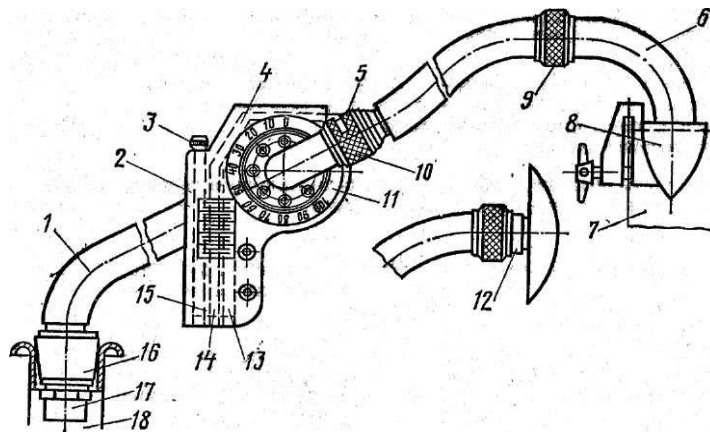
Загальний вигляд і схема підключення газового витратоміра КИ-4887-ІІ. 1 - трубопровід; 2 - манометр; 3 - пробка; 4 - корпус газорасходомера; 5 - дросель; 6 - трубопровід; 7 - вихлопна труба двигуна; 8 - ежектор; 9 - муфта сполучна; 10 - заслінка; 11 - маховичок; 12 - змінний ежекторний пристрій; 13 - правий канал; 14 - середній канал; 15 - лівий канал; 16 - наконечник; 17 - забірний патрубок впускного трубопроводу; 18 - маслозаливна горловина.
